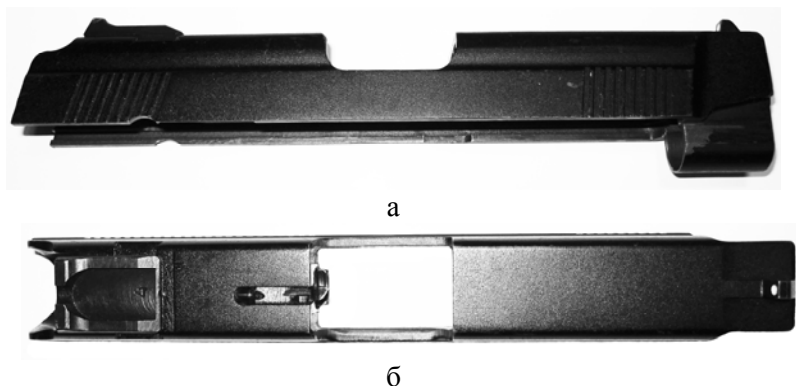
Кожух-затвор: а – вид сбоку; б – вид сверху
